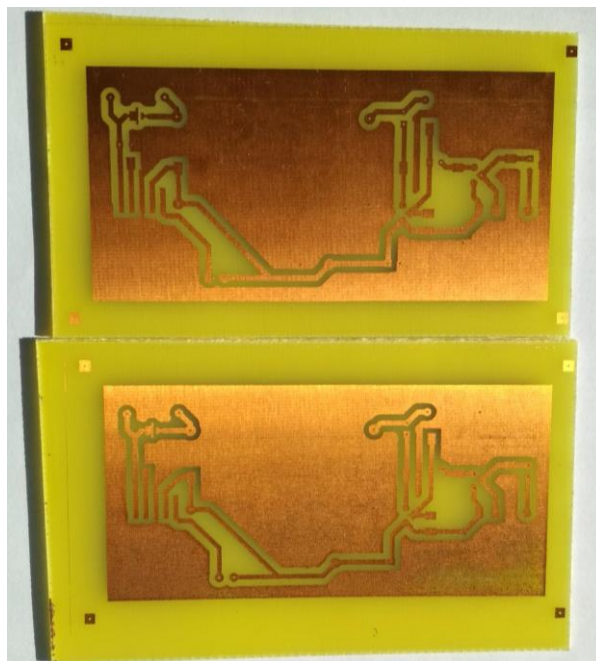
Resultado del revelado de la PCB del Transmisor.
